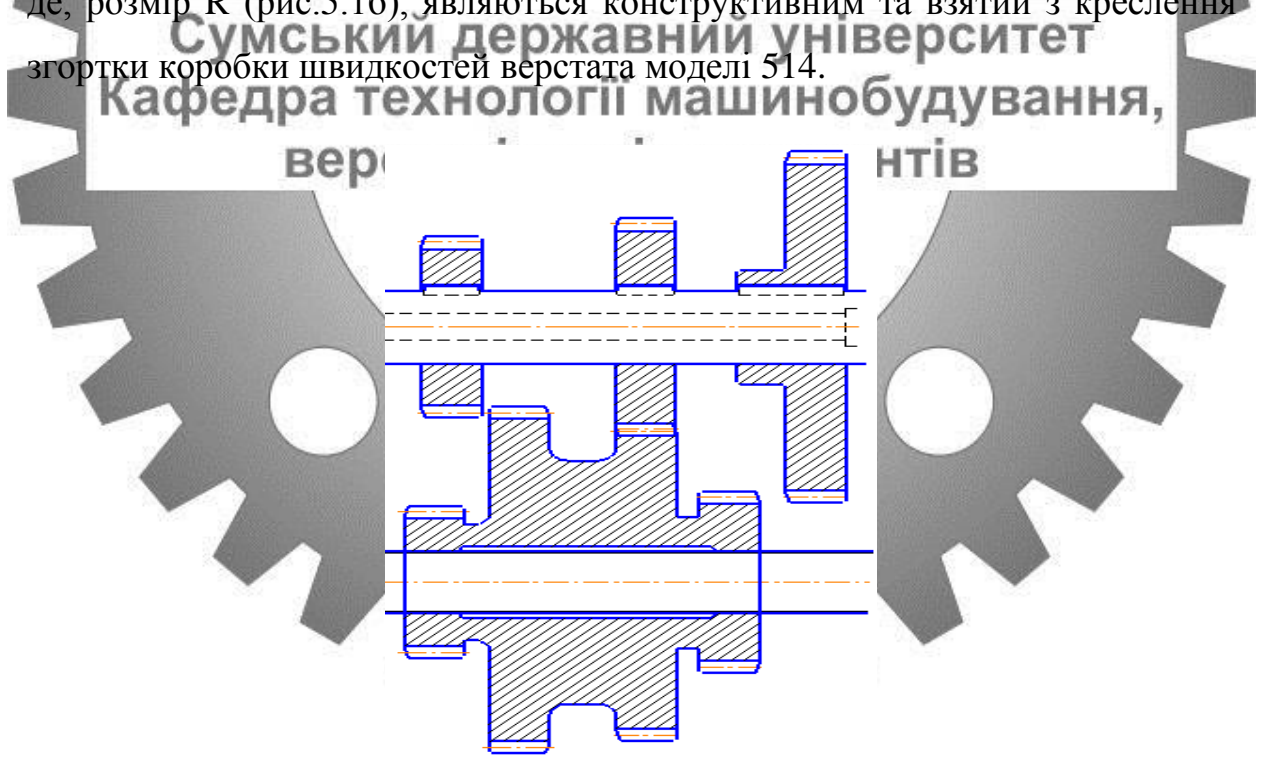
Конструктивна схема переміщення та положення блока зубчатих коліс БЗ– зачеплення Z80/Z40.
